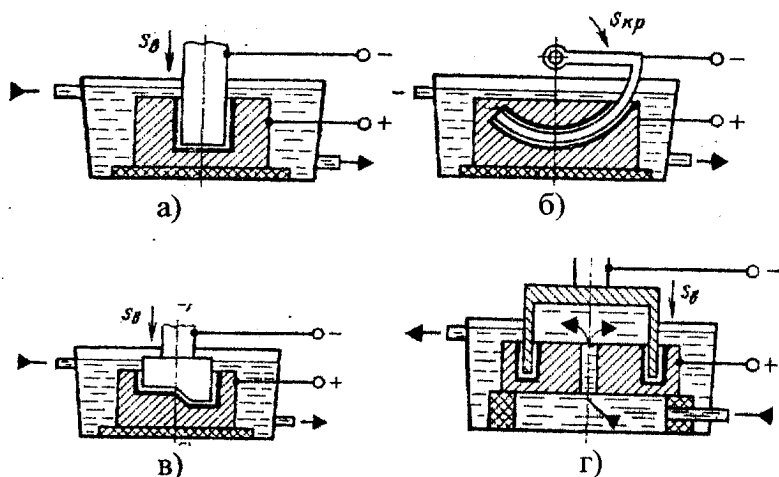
Деякі схеми електроіскрової обробки:
